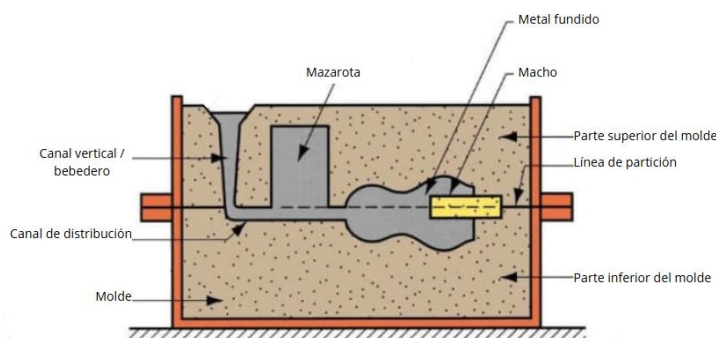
Componentes del proceso de fundición en molde de arena [14].
